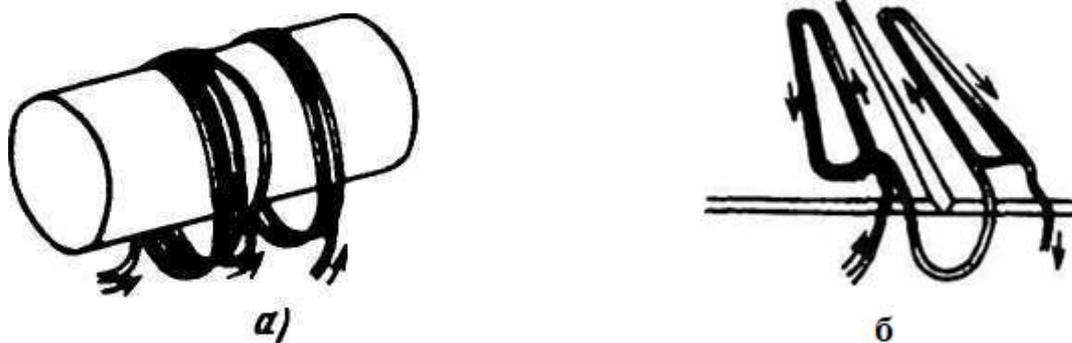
Схема размещения сварочных кабелей при размагничивании (стрелками указано направление тока) : а – при сварке трубопроводов; б – при сварке листовых конструкций
